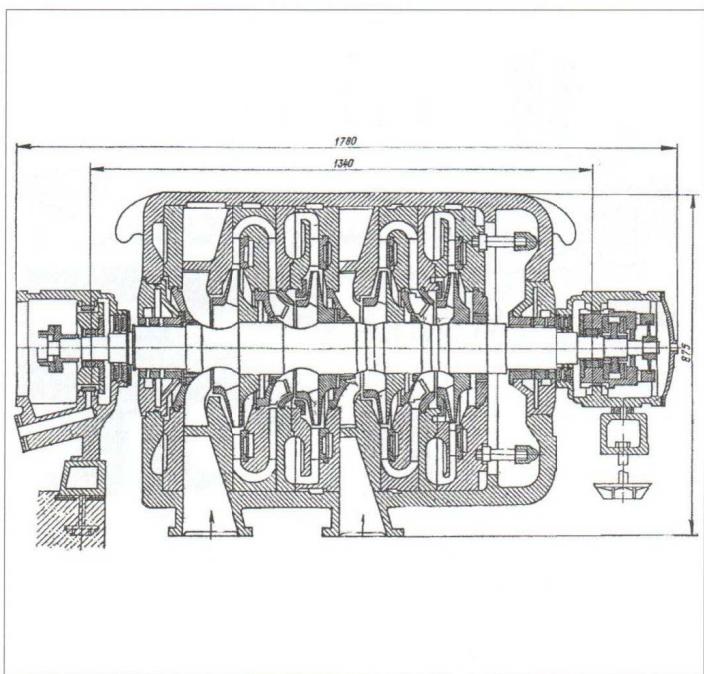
Конструкция типового корпуса сжатия центробежного компрессора УЦКМ СКБК-ККЗ
